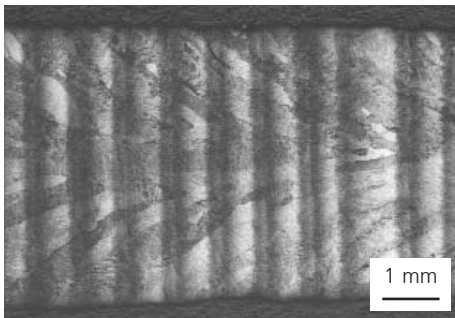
Querschliff einer Mehrlagen-Auftragschweißung aus Ti6242
